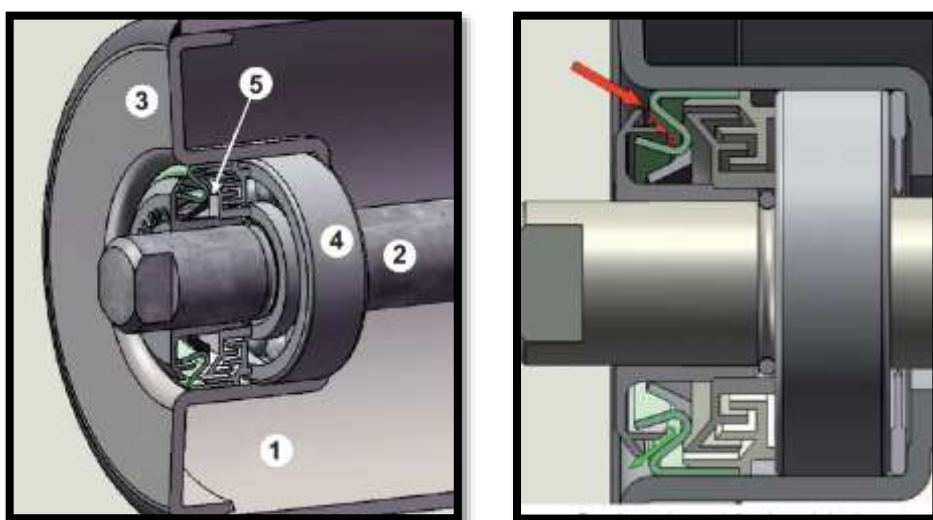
Detalle obturador de las partes rodantes del rodillo.
